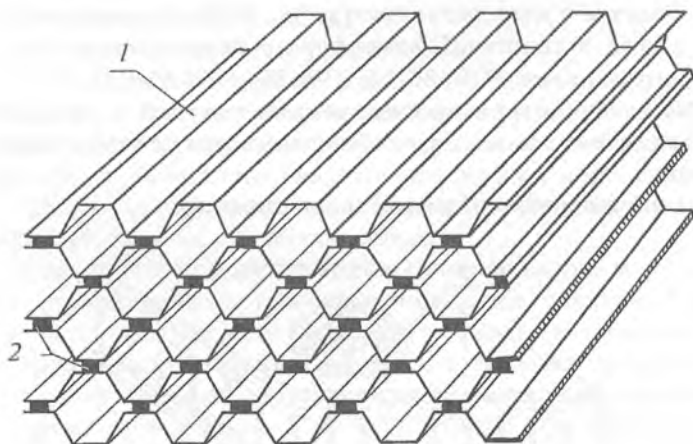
Сотовый блок: 1 — фольга; 2 — припой
